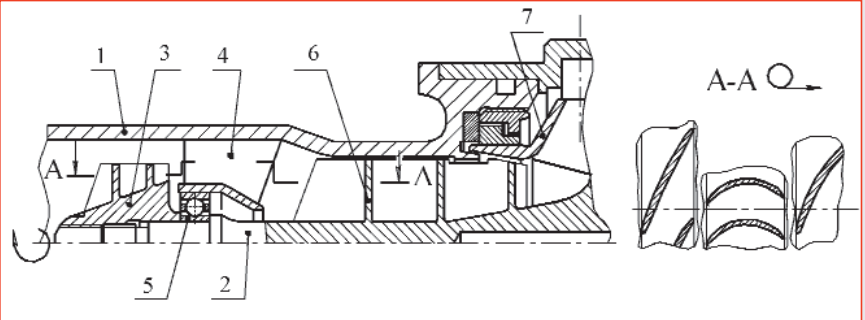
1 - корпус насоса, 2 - вал, 3 - бустерный шнек, 4 - пилоны, 5 - подшипник, 6 - предвключенный шнек, 7 - центробежное колесо
